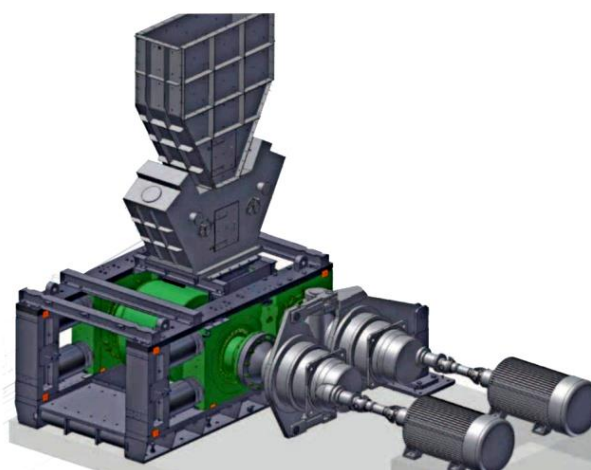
Schemat budowy i działania młyna PREMILL: 1 – wałek główny dolny ze stałymi oprawami łożysk, 2 – walce górne, 3 – oprawy ruchome, 4 – układ hydrauliczny docisku rolek, 5 – konstrukcja wsporcza głównego walca, 6 – zbiornik nadawczy (źródło: opracowanie własne na podstawie [5])
